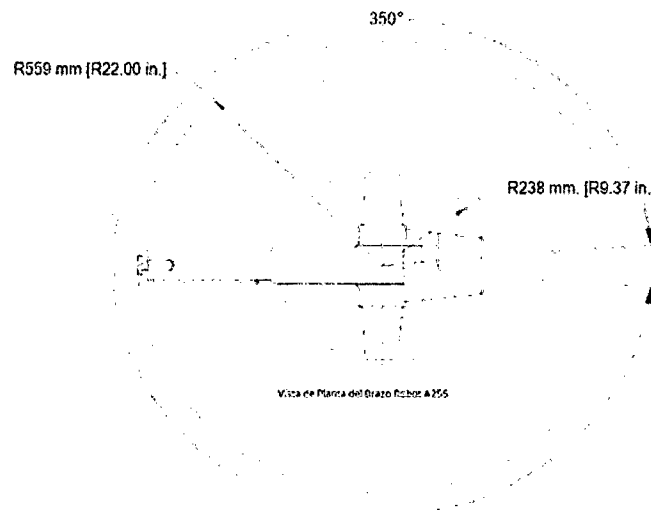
Espacio de trabajo vista de planta del brazo robot A255
